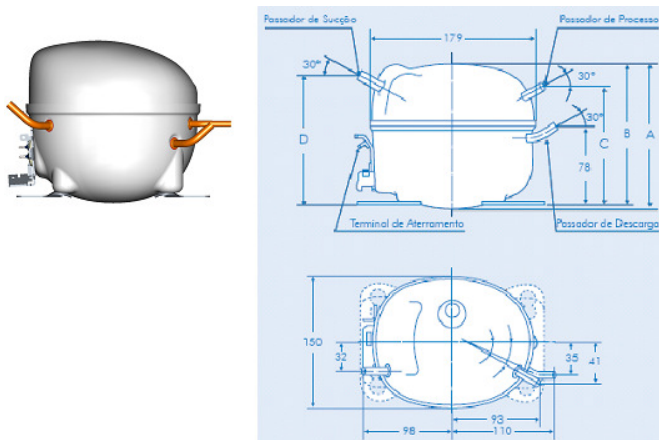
Dimensões da carcaça do compressor para refrigeração doméstica.
